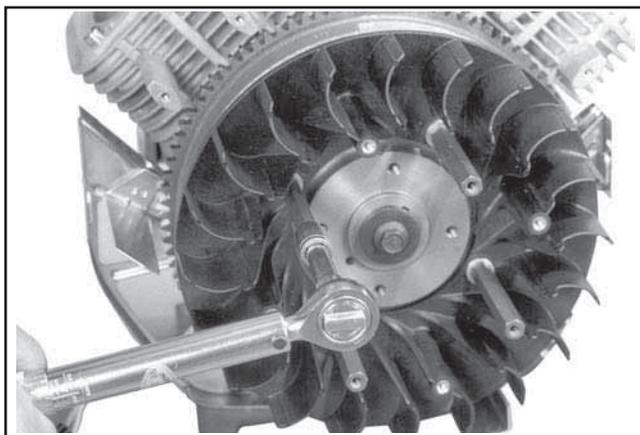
Serrage des supports de la grille de protection en métal (certains modèles).
